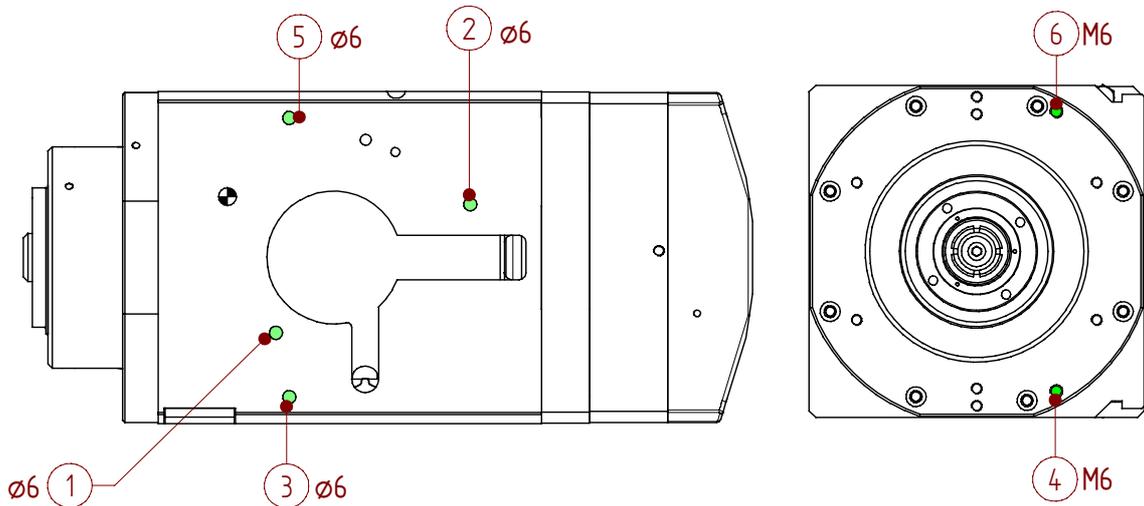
hydraulische anschlüsse für ES789 mit Befestigungsbohrungen
